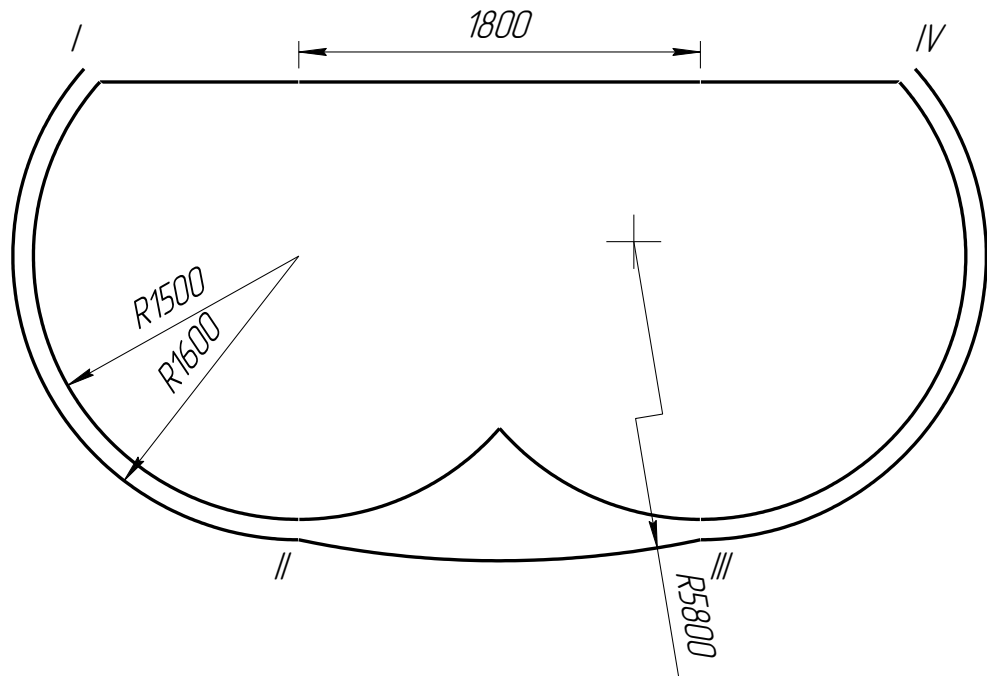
Поперечний переріз корпусу і парової камери
